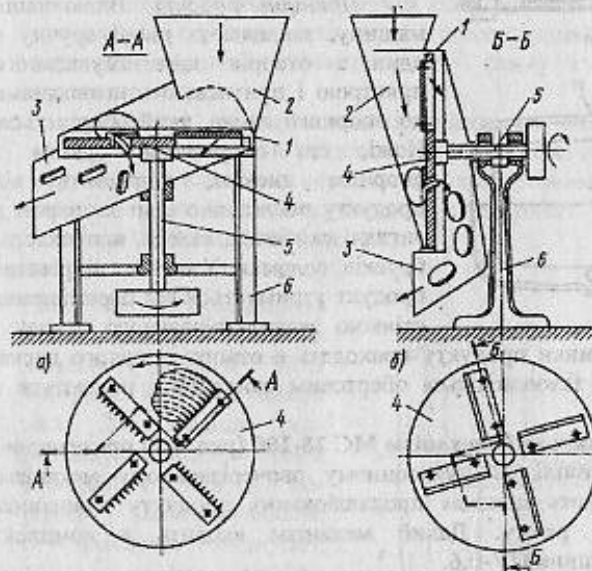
Схеми дискових овочерізок: а – з горизонтальним диском; б – з вертикальним диском; 1 – циліндр пустотілий; 2 – завантажувальний пристрій; 3 – розвантажувальний лоток; 4 – опорний диск; 5 – вал приводний; 6 – станина
